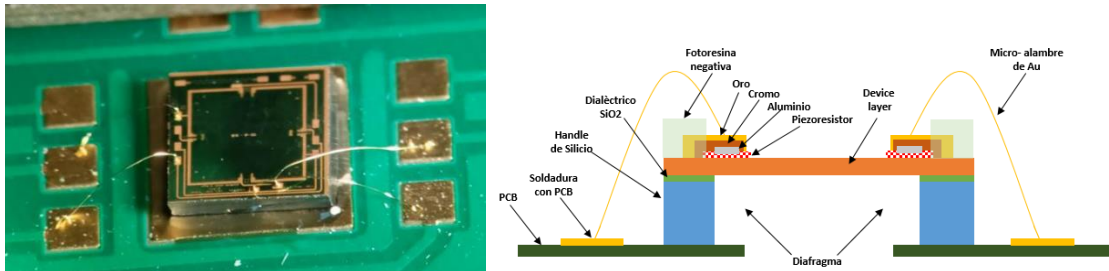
Pegado y micro-soldado del chip a la PCB.
